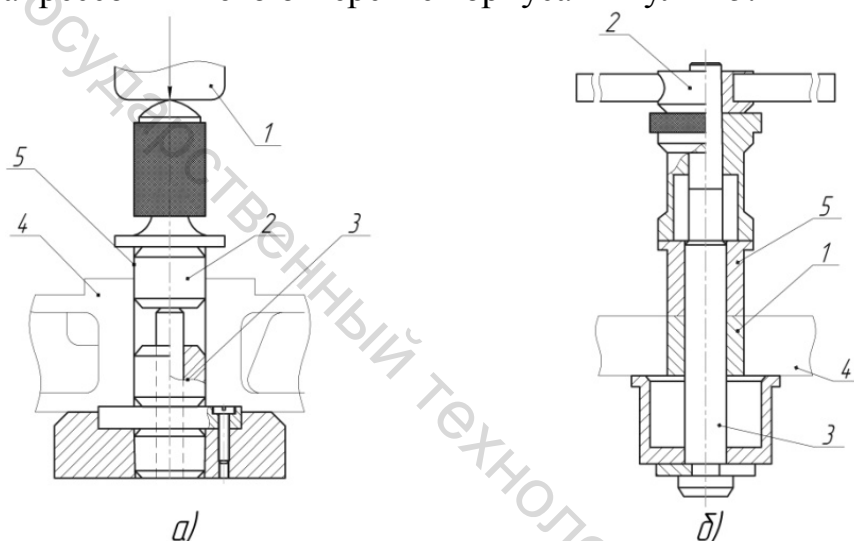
Запрессовка подшипников в виде втулок:
